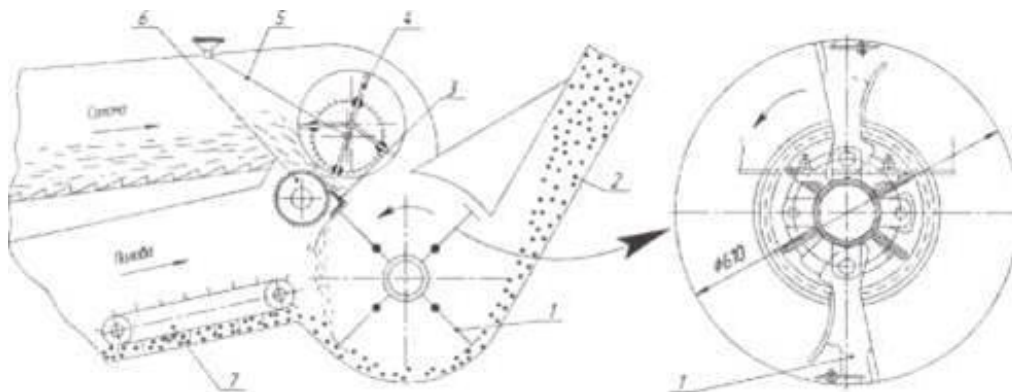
Принципиальная конструктивно-технологическая схема измельчителя ИСН-3,5: 1 - молотковый барабан; 2 - трубопровод; 3 - противорежущее устройство; 4 - верхний валец; 5 - механизм шарнирной подвески верхнего вальца; 6 - нижний валец; 7 - транспортер половы.
